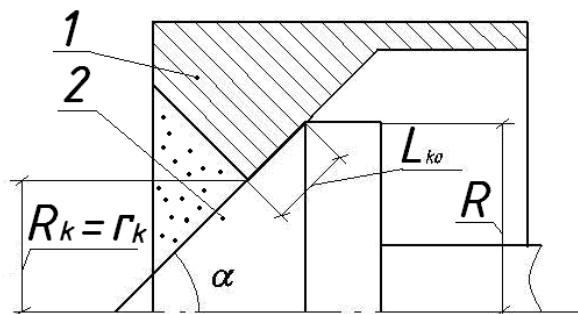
Положення робочої частини головки екструдера на початку роботи: 1 – робоча поверхня корпусу екструдера; 2 - конус головки екструдера який закриває робочу зону.
